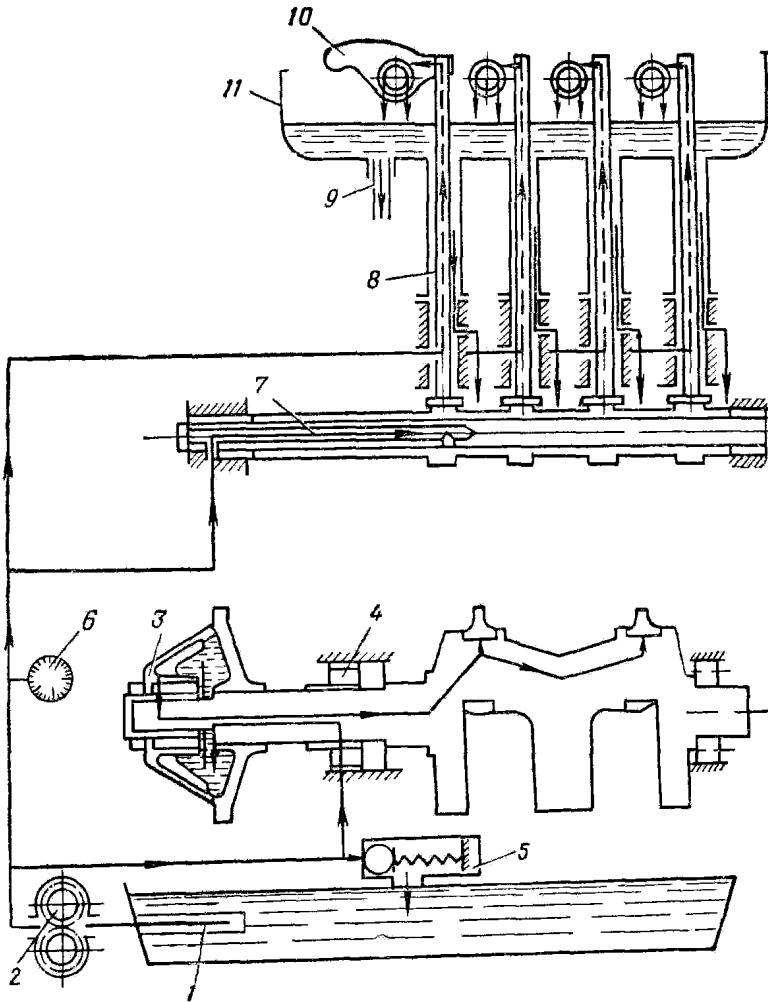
Схема системы смазки двигателя УД-25Г:
